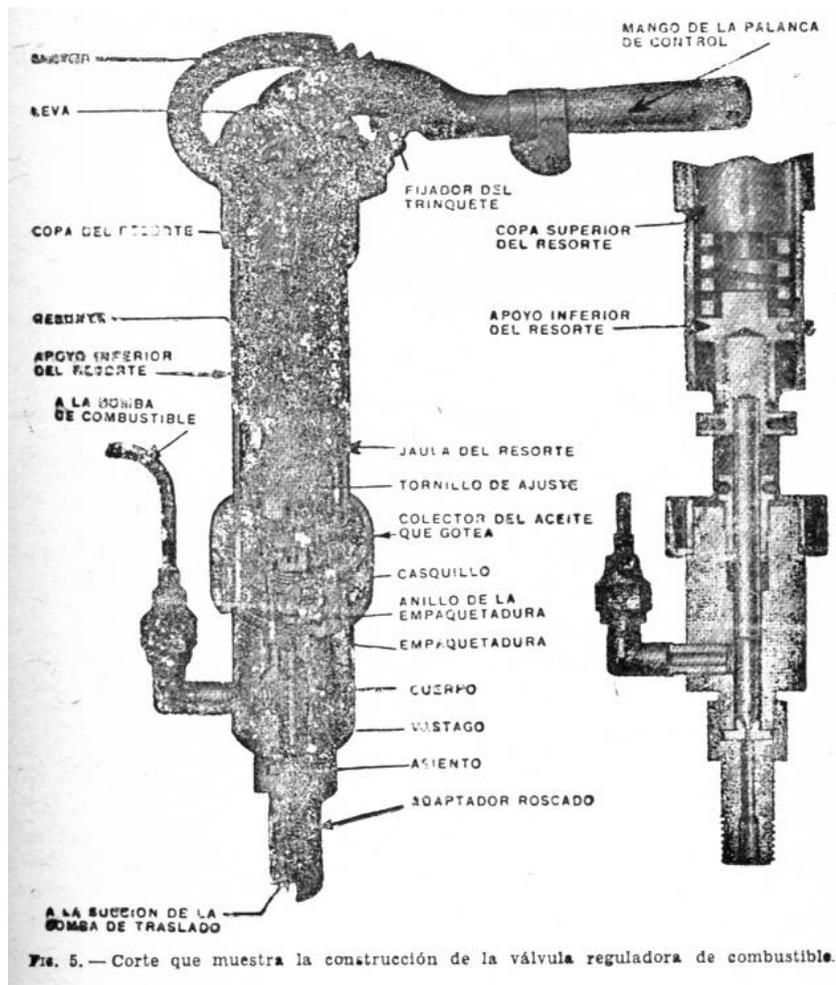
Corte que muestra la construcción de la válvula reguladora de combustible.
